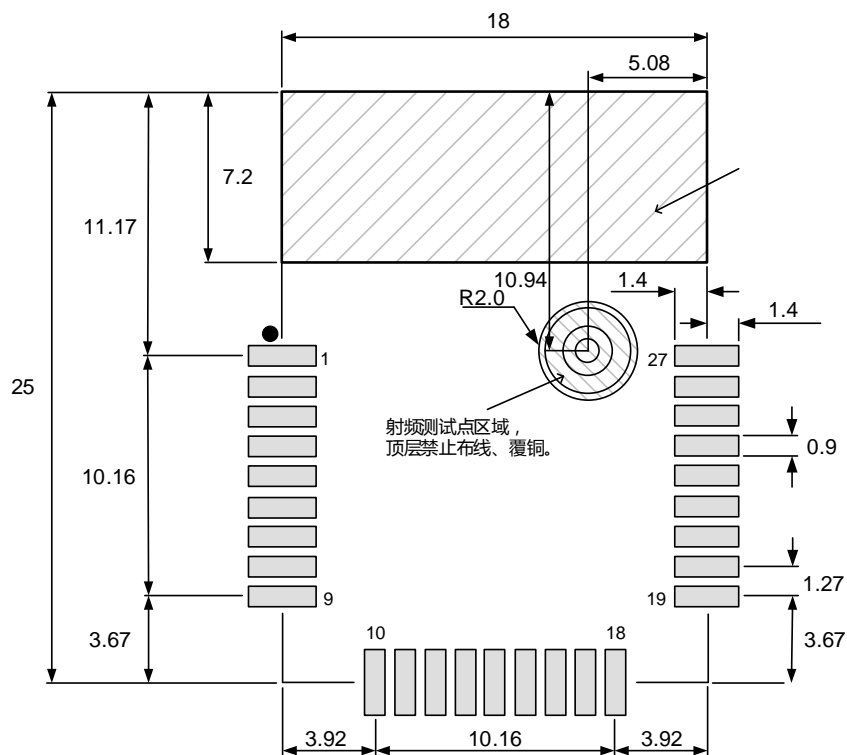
ZM5955P 和 ZM5955E 推荐 PCB 封装尺寸
